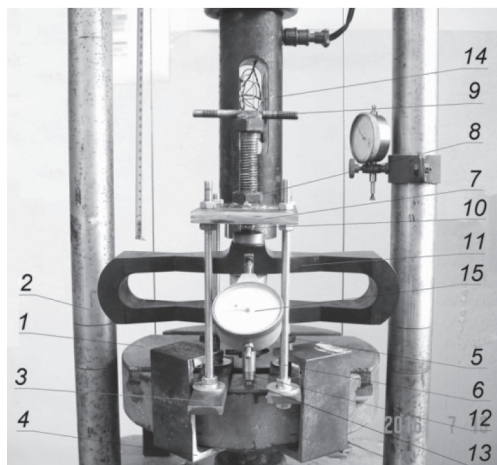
Общий вид нажимного устройства для испытания на прочность инструментальных материалов: 1 – нижняя плита пресса; 2 – стойка пресса; 3 – планка; 4 – зажим винтовой; 5 – болт зажимной; 6 – болт стяжной; 7 – пластина; 8 – гайка приварная; 9 – винт с ручкой для вращения; 10 – шарик; 11 – динамометр; 12 – проставка давяльная с твердосплавной вставкой; 13 – испытуемый образец; 14 – датчик усилия зажима испытуемого образца; 15 – индикатор часового типа
